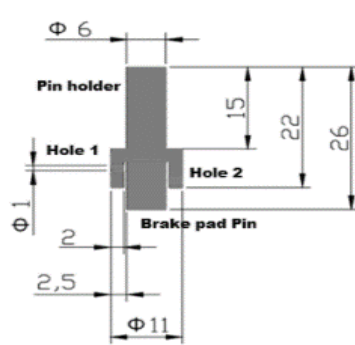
Dimensiones del pasador y del soporte del pasador.
